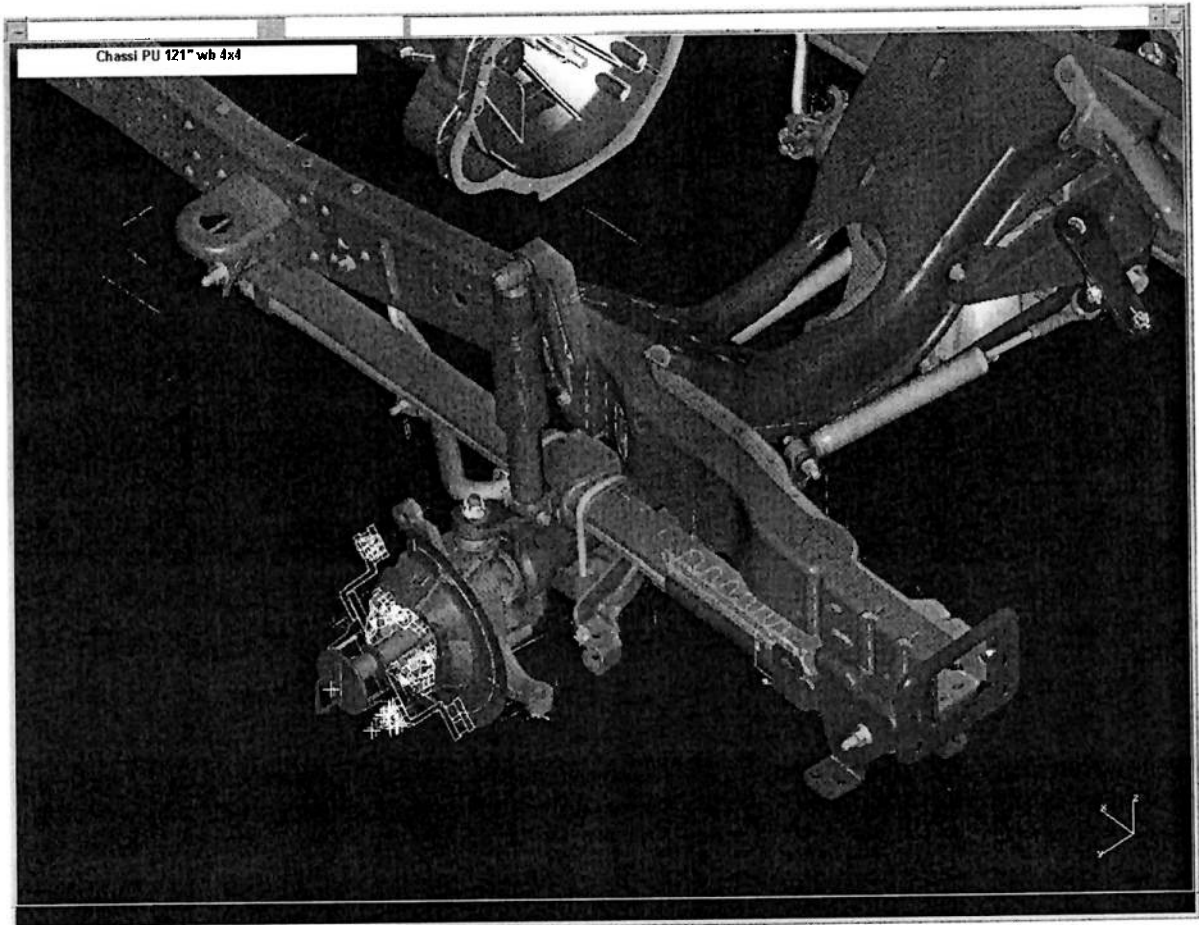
Chassi PU 121''wb 4x4 – Conjunto Dianteiro
